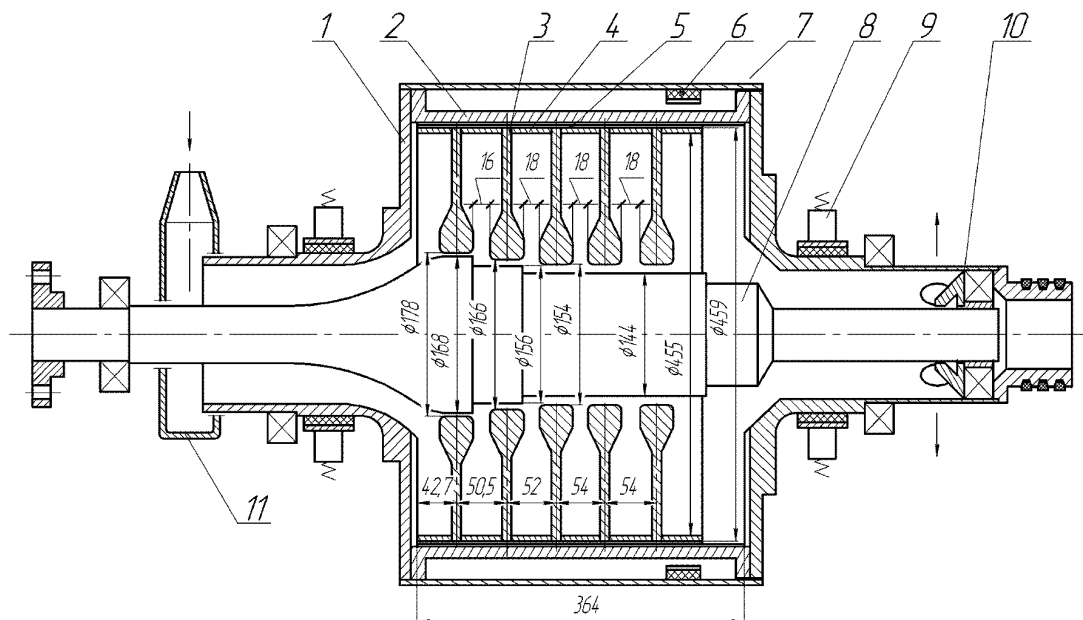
Рабочий участок экспериментального стенда: 1 – полувал левый; 2 – барабан; 3 – диск; 4 – проставочное кольцо; 5 – внутренний электронагреватель; 6 – внешний электронагреватель; 7 – защитный кожух; 8 – центральный вал; 9 – медно-графитовые щетки; 10 – полувал правый; 11 – воздухоподводящее устройство
